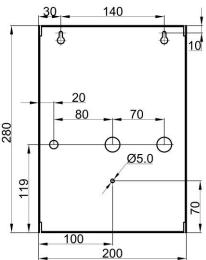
Габаритно-установочные размеры (вид спереди)
